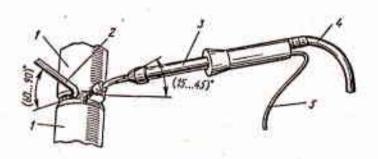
Сварка пластмассовых труб нагретым газом с присадочным материалом;
